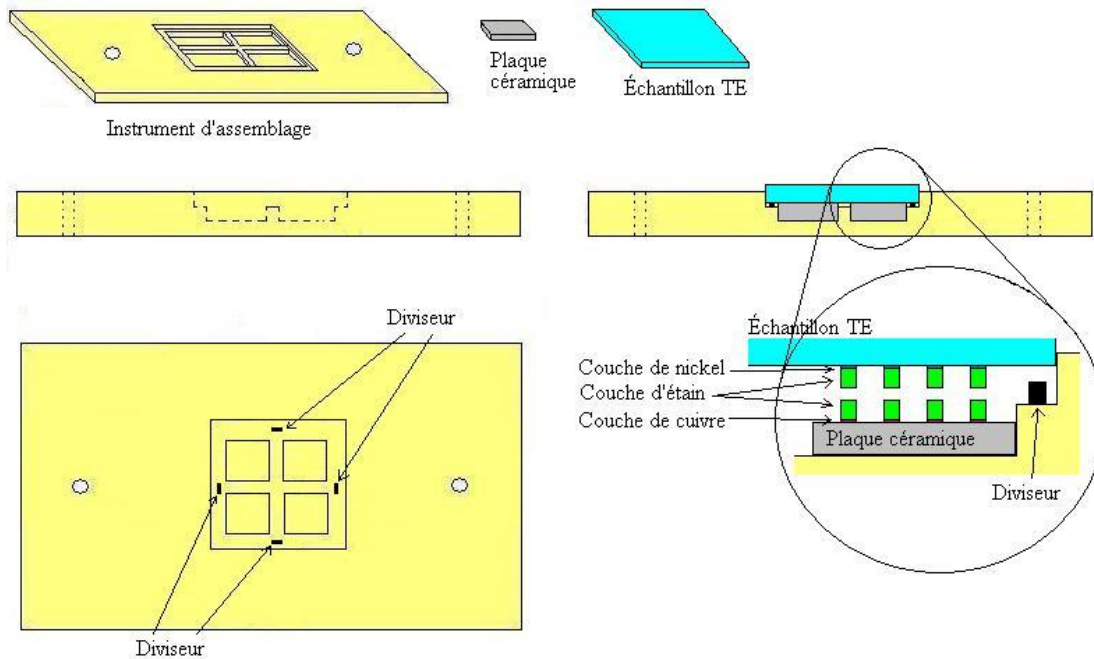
Instrument utilisé pour la première soudure.
